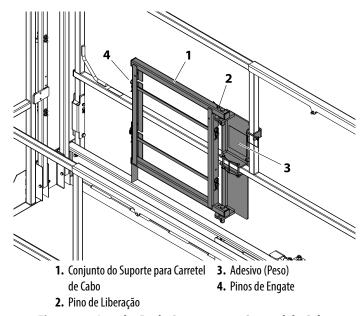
Instalação do Suporte para Carretel de Cabo
